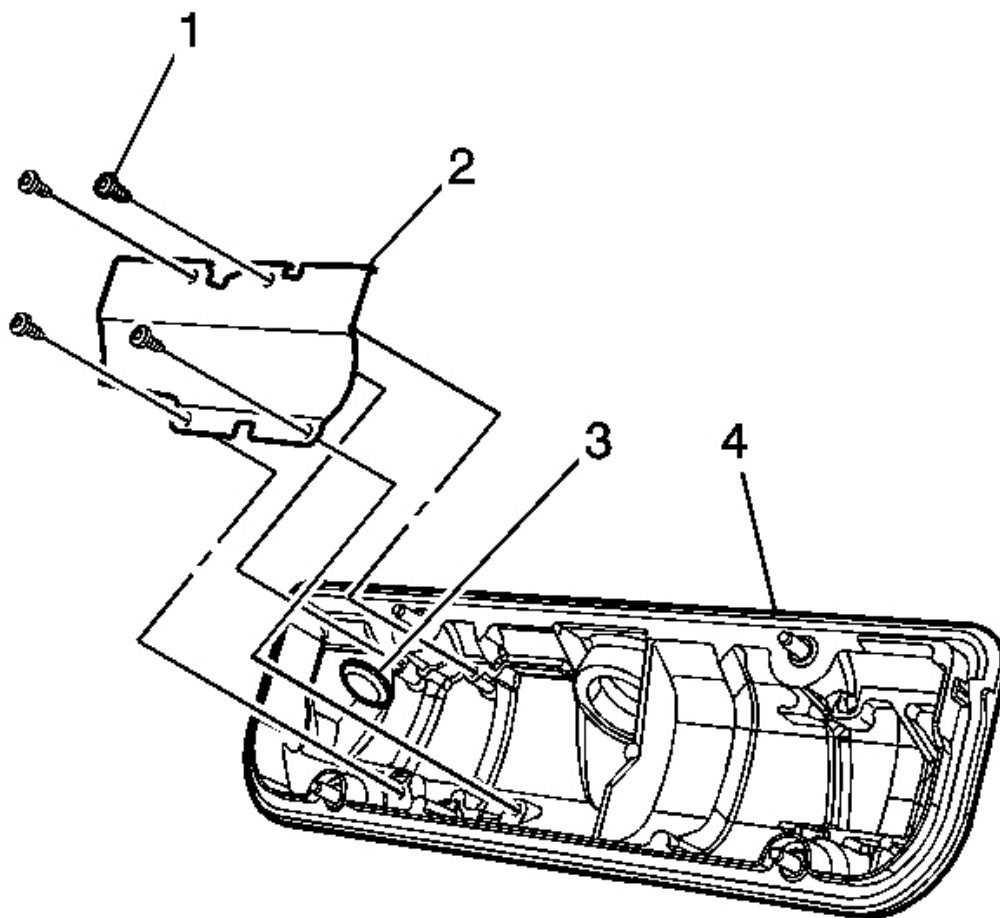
Vista de la válvula cubierta de balancines - Cortesía de General Motors Corp Izquierda.
